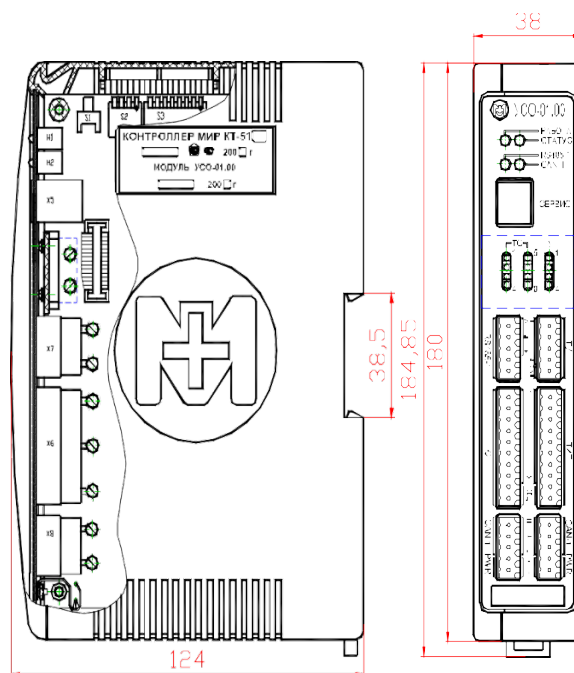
Внешний вид и габаритные размеры модуля УСО-01
